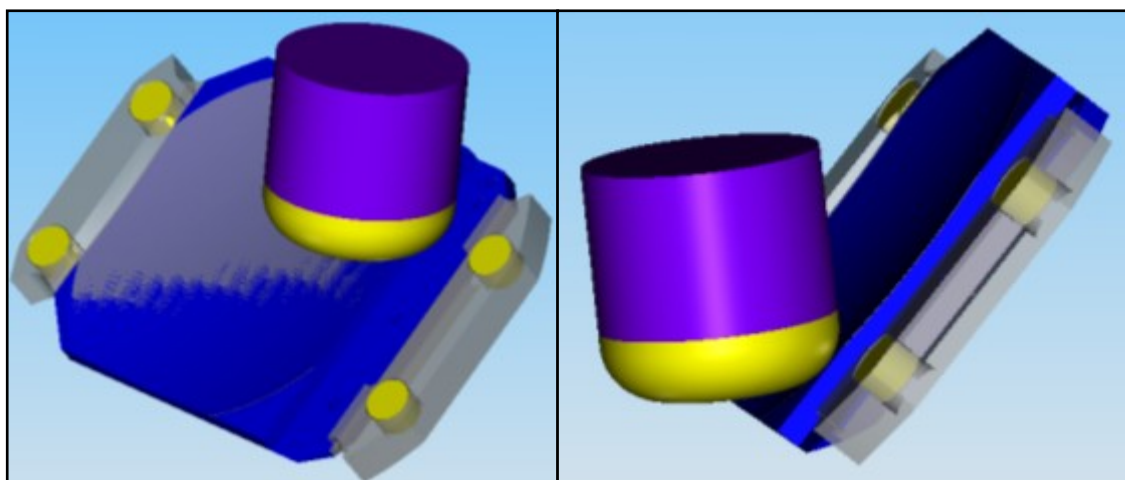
Frézování na čisto s bočním krokem 0,21 mm; č. op. 180.
